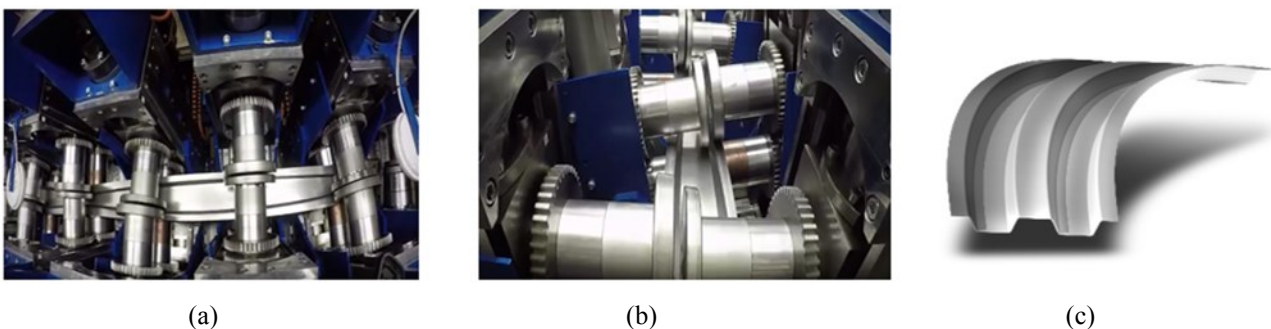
Flexible Walzprofilieranlage mit höhenveränderlichen Profilergerüsten [8] (a) + (b); Multiaxial gekrümmtes Bauteil [8] (c)
